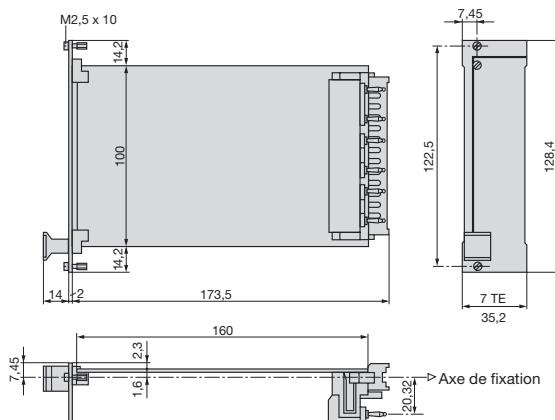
EURAX UI 505, largeur de la plaque frontale 7 TE.
